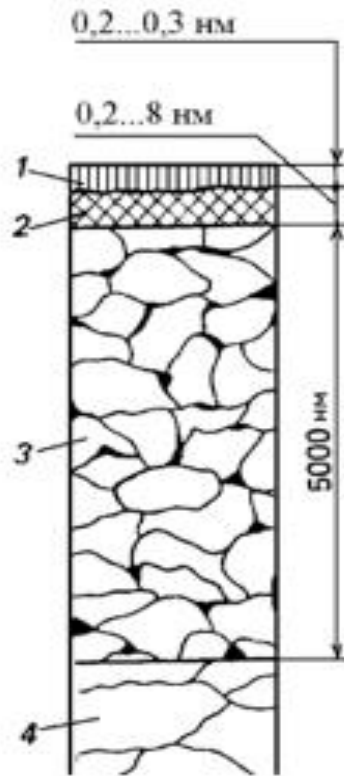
Структура поверхностного слоя шлифованной детали из углеродистой стали
